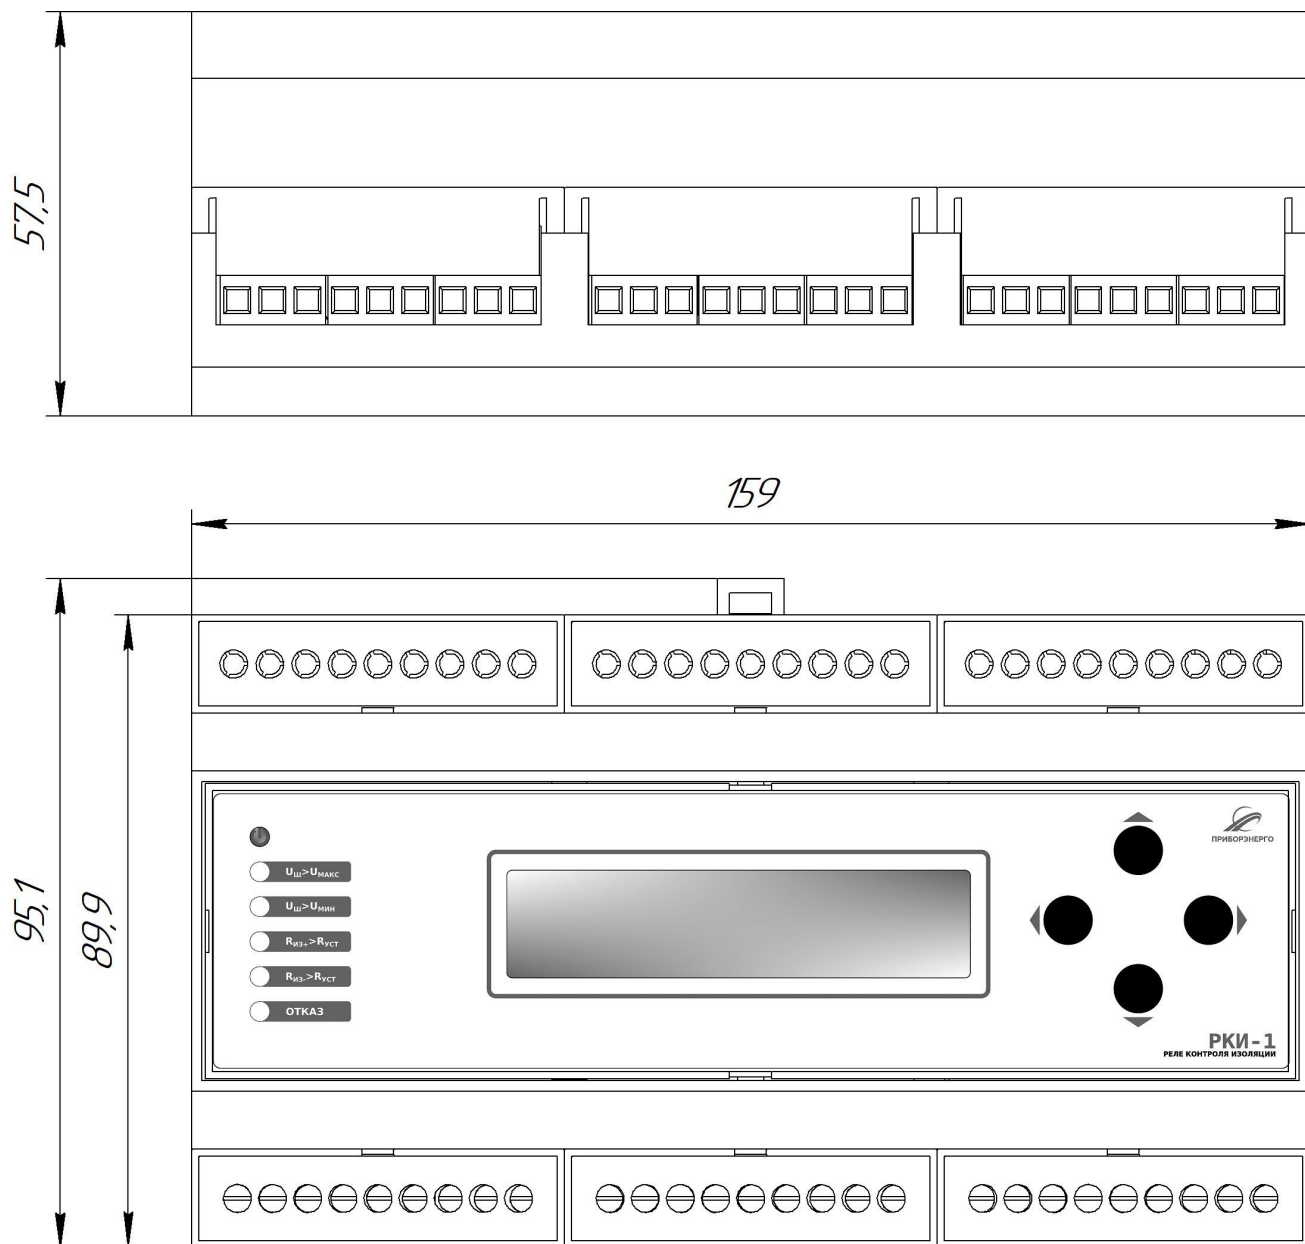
Габаритные размеры реле контроля изоляции РКИ-1
